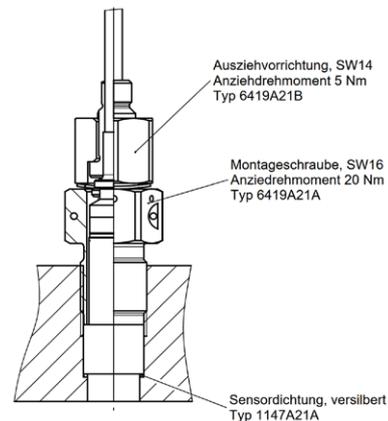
Montage mit Montageadapter Typ 6419A21A, Dichtung Typ 1147A21A und Ausziehvorrichtung Typ 6419A21B
